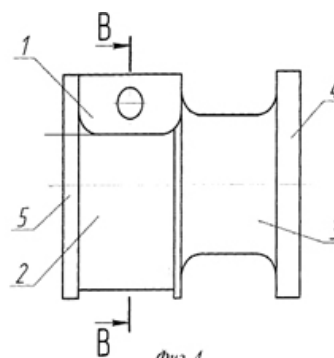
Вид спереди на опорную стенку и шейку насосной секции
